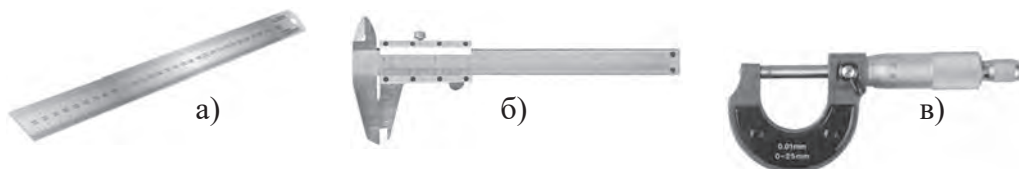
Инструменты для измерения со шкалой: а – линейка; б – штангенциркуль; в – микрометр.
